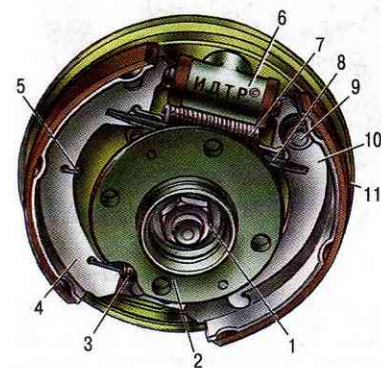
Тормозной механизм заднего колеса: 1 - гайка крепления ступицы; 2 - ступица колеса; 3 - нижняя стяжная пружина колодок; 4 - тормозная колодка; 5 - направляющая пружина; 6 - колесный цилиндр; 7 - верхняя стяжная пружина; 8 - разжимная планка; 9 - палец рычага привода стояночного тормоза; 10 - рычаг привода стояночного тормоза; 11 - щит тормозного механизма
